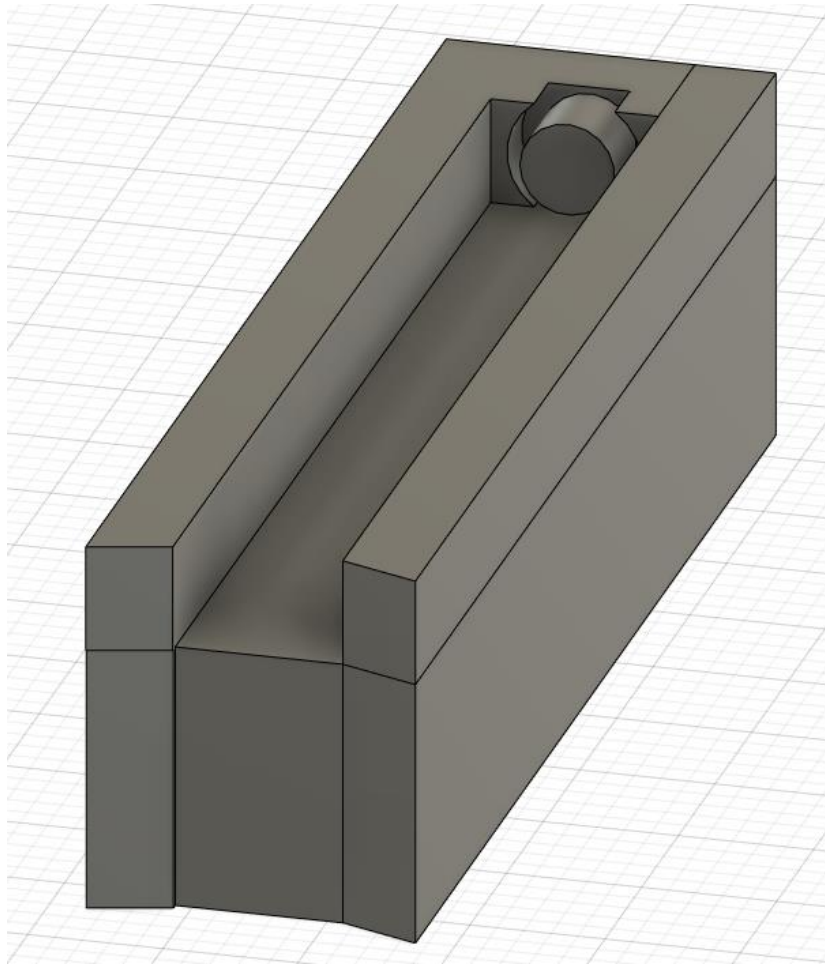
Додатковий корпус для направлення та утримання стопорного штифту у правильному положенні
